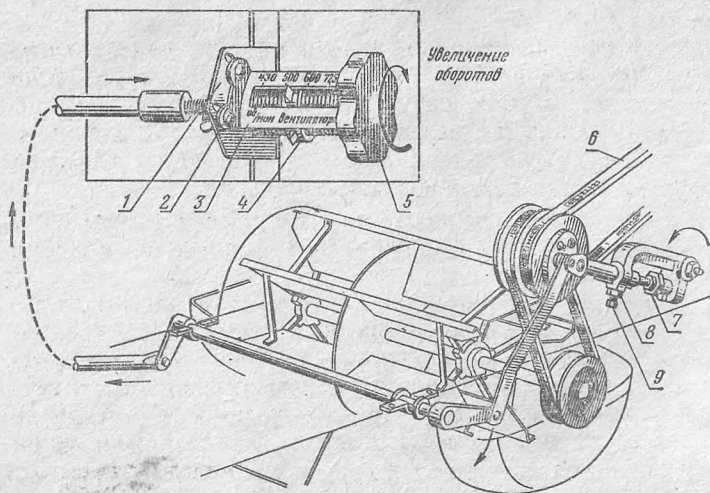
Регулировка механизма управления вариатором вентилятора очистки:
